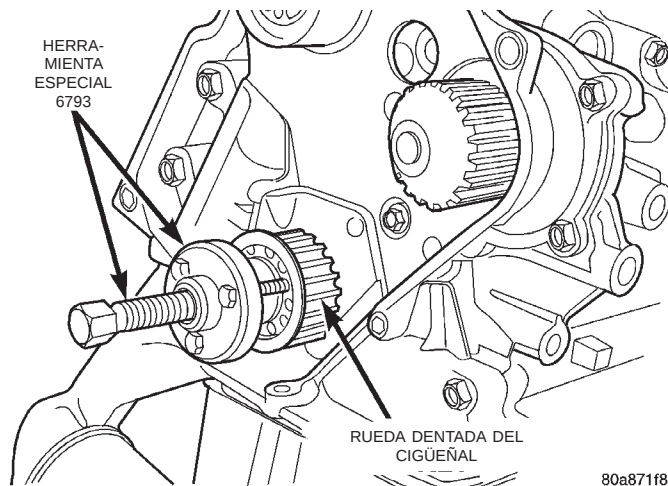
Rueda dentada del cigüeñal—desmontaje
